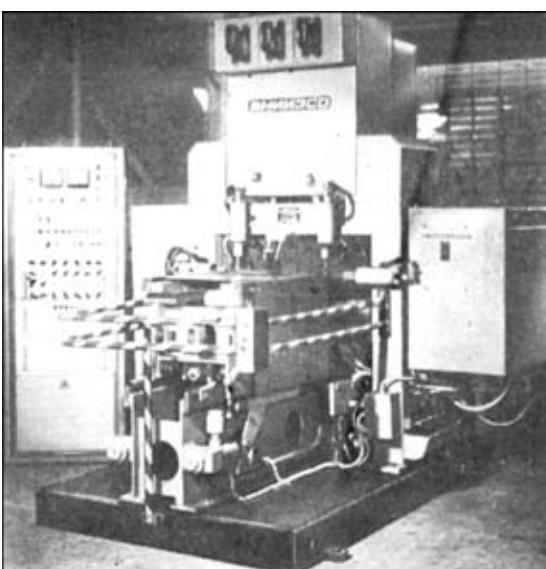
Установка для односторонней точечной сварки кожухов сварочных трансформаторов УТМ-01 (Ленинград, ВНИИЭСО, 1983)
